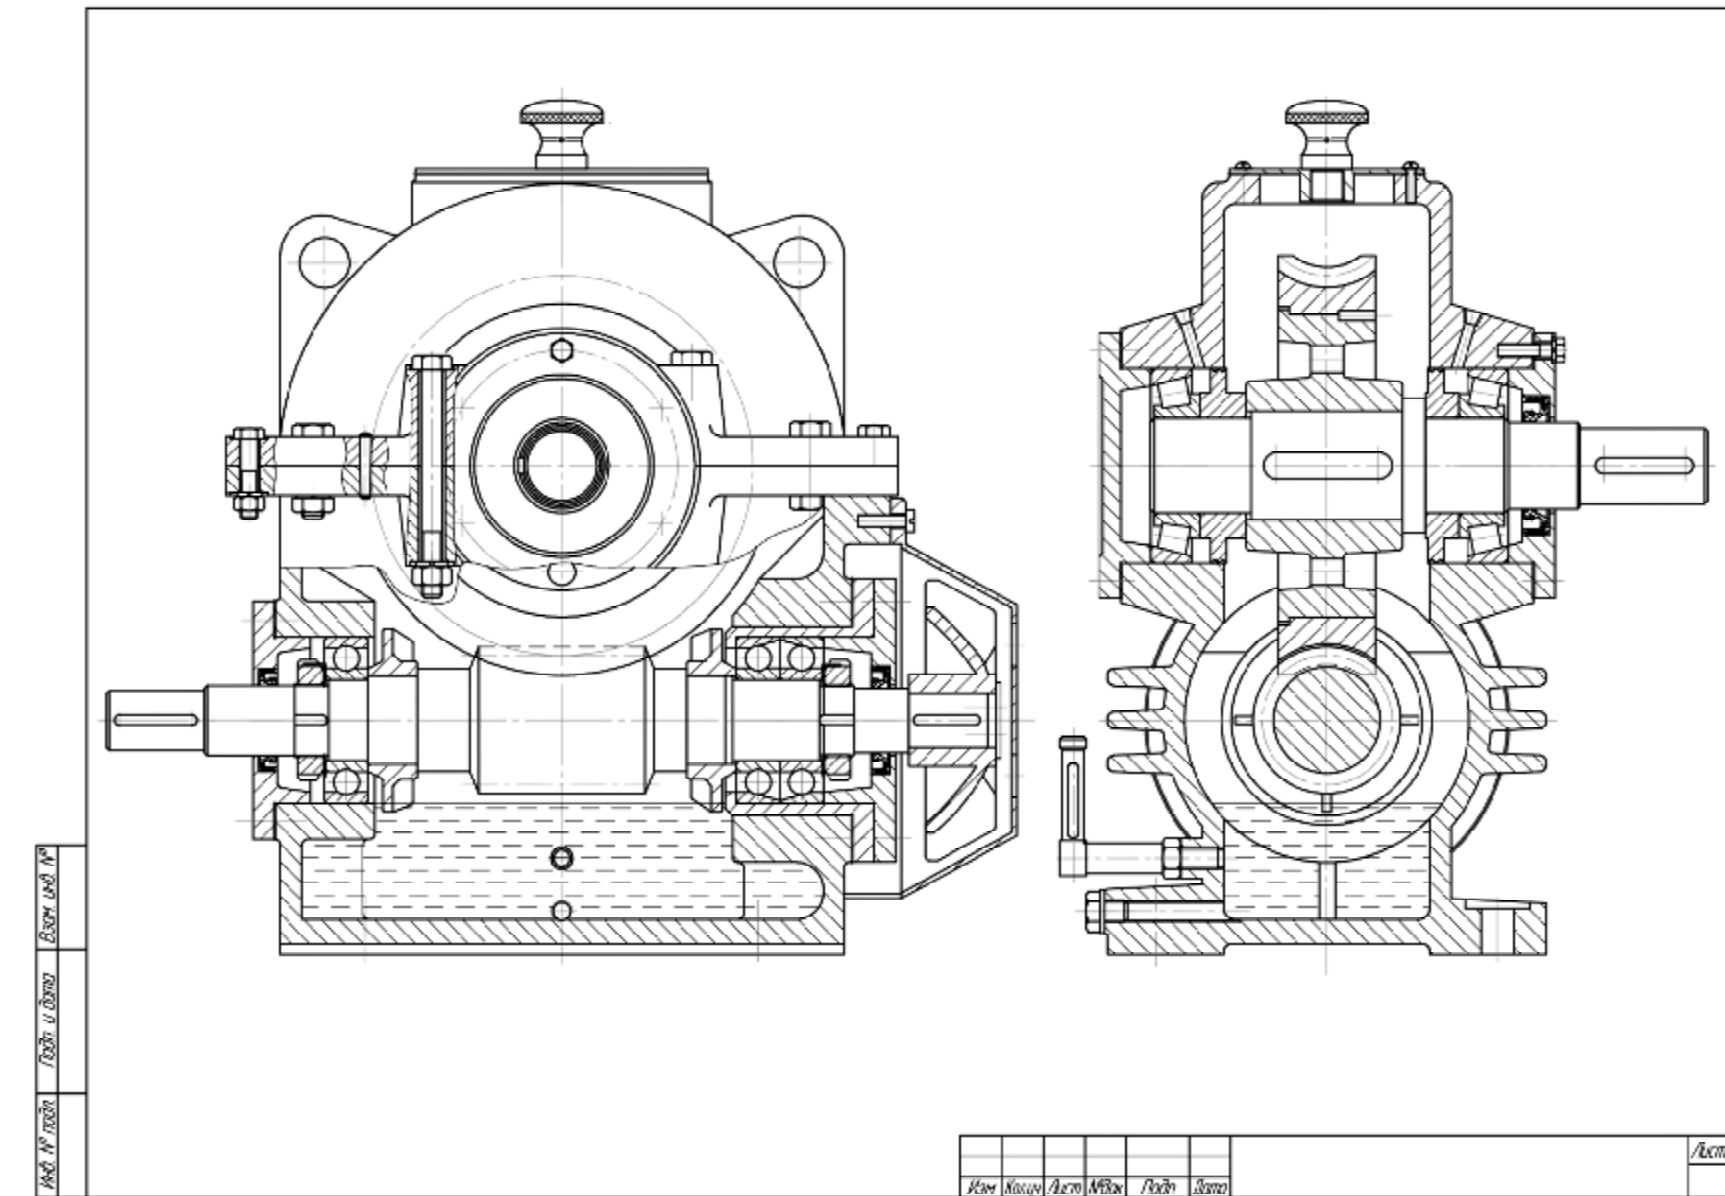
Редуктор червячный с нижним расположением червяка
